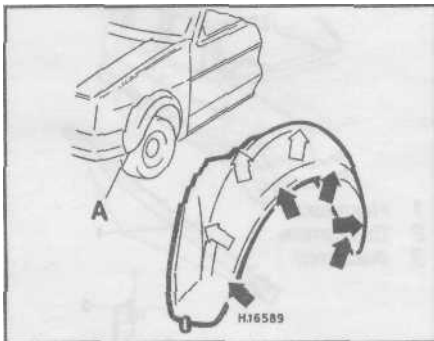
Расположение винтов крепления локеров колеса [показаны стрелками]
